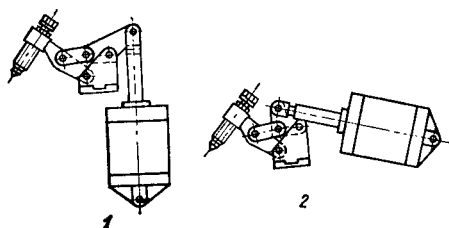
Типовые компоновки пневматических прижимов сборочно-сварочных приспособлений (1, 2 — варианты прижимов)
